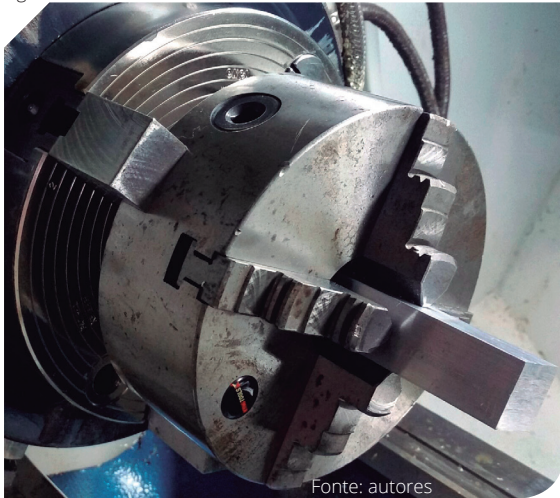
Placa mecânica de 3 castanhas adaptada em placa pneumática
